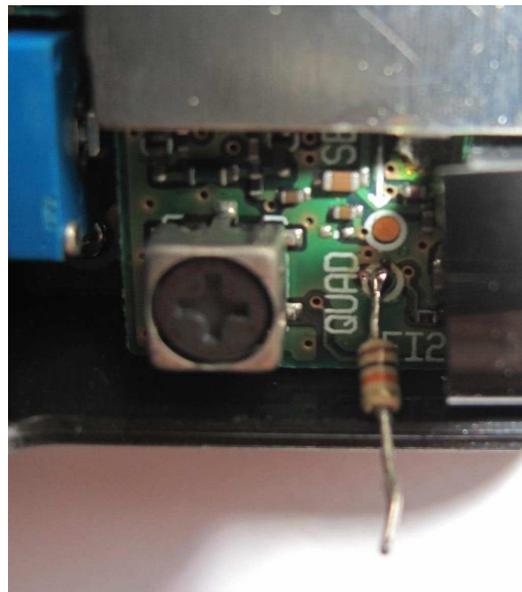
La résistance ajoutée de 10 kΩ soudée sur le point « QUAD ».
